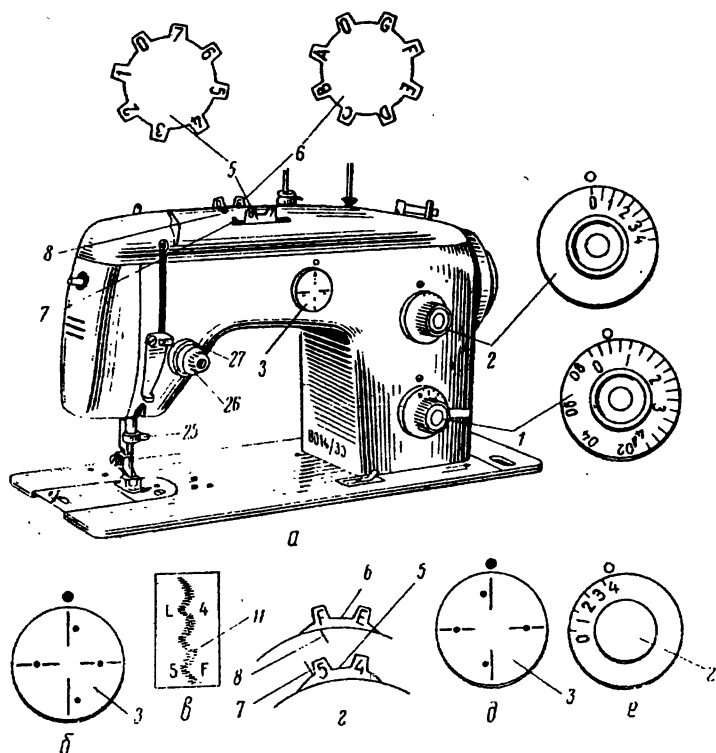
Работа с автоматикой на машине «Веритас» 8014/33 класса: а — расположение звезд автоматикой на машине, обозначение зубьев; установка рычага 1 управления для узорной строчки; б — установка рычага 3 для вращения буквенной звезды; в — выбранный по таблице или специальной ленте узор; г — установка зубьев звезд автоматикой; д — установка рычага 3 согласно выбранному узору; е — установка рычага 2 согласно выбранному узору
